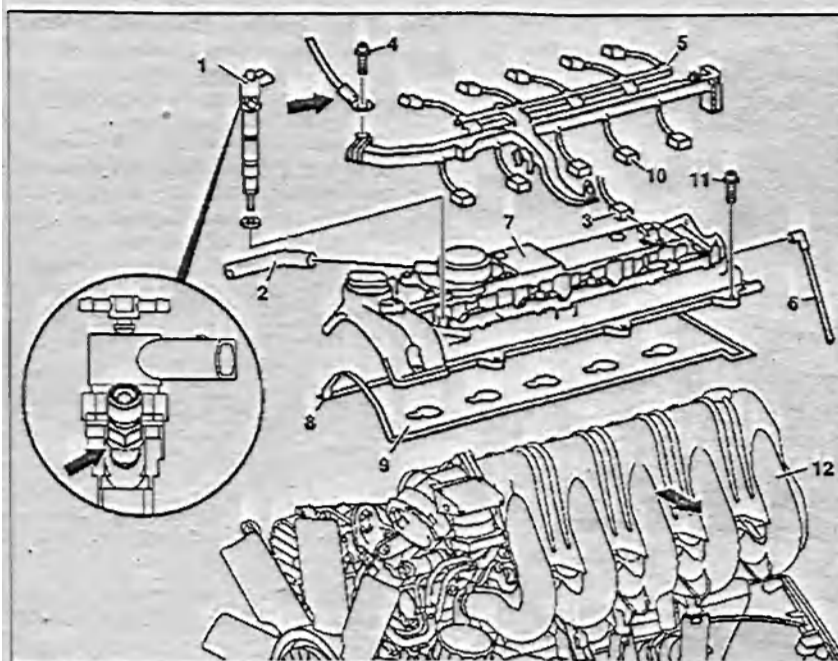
Снятие и установка крышки головки блока цилиндров на двигателях 612.981:
